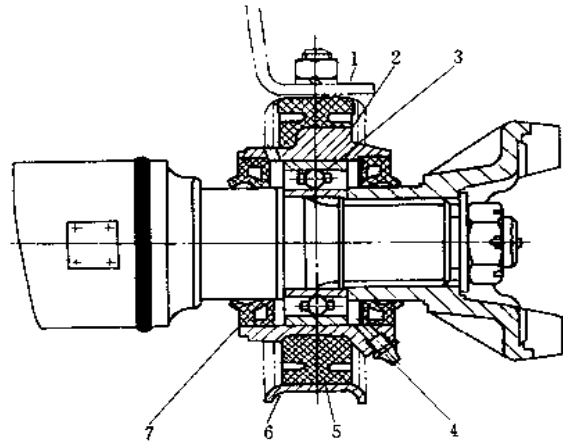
东风 EQ1090E 型汽车传动轴中间支承
